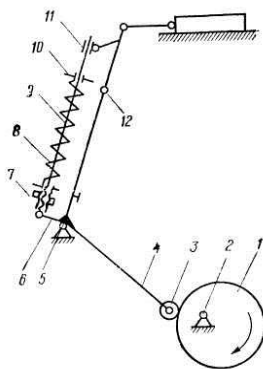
Схема приводу нагнітаючого поршня тістоподільної машини РМК: 1 – кулачок, 2 – вал, 3 – ролик; 4, 6 – важелі; 5 – вісь; 7 – тарілчаста гайка; 8 – пружина; 9 – качалка; 10 – тарілка; 11 – обойма; 12 – шарнірне з'єднання
